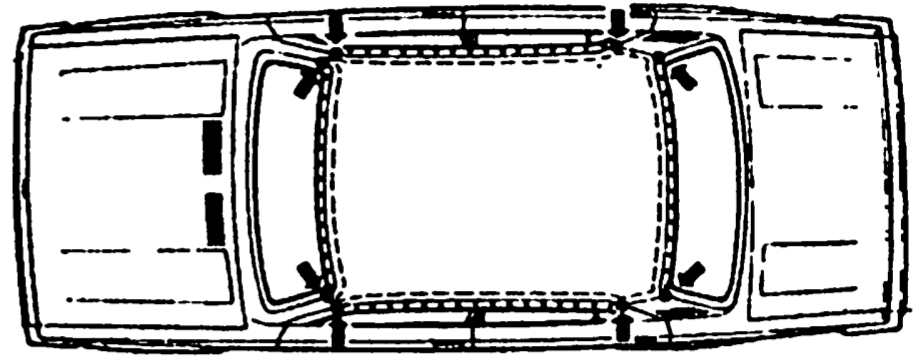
Места сварки крыши. Точками обозначены швы контактной сварки. Стрелками показаны места газовой сварки
